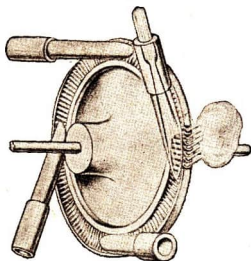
Laufrad einer Dampfturbine mit Laval-Düsen
